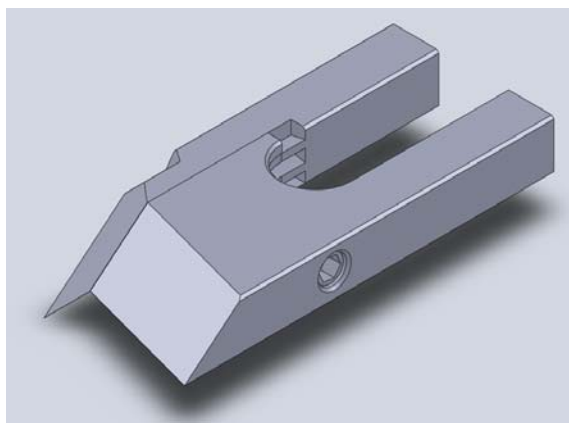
Сборный двухлезвийный нож фрезерно-брусующего станка
